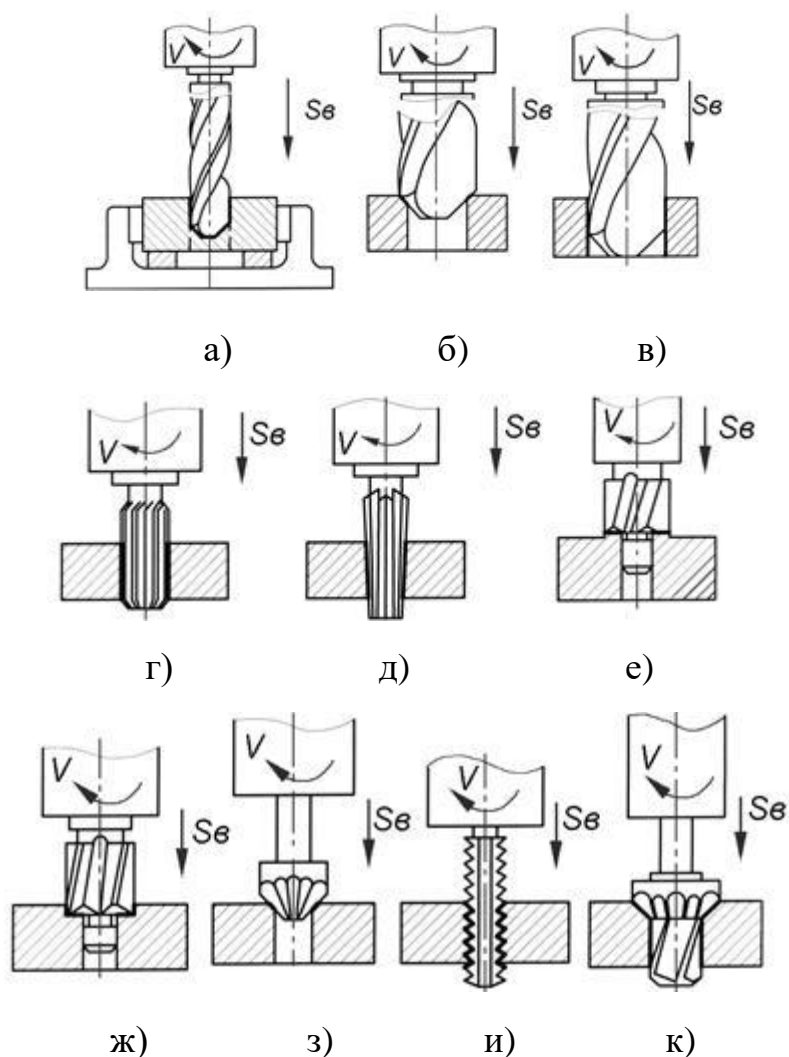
Схемы обработки поверхностей на сверлильных станках
